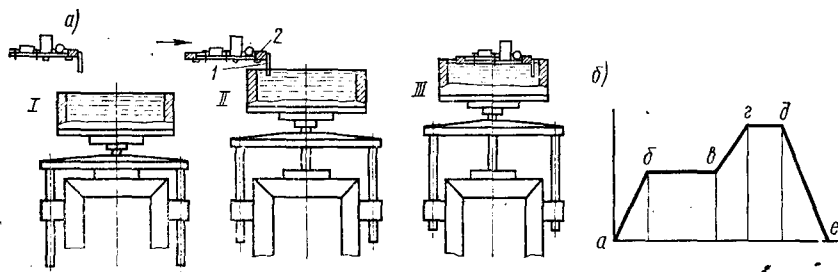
Схема устройства для групповой пайки со шлакоудалителем
